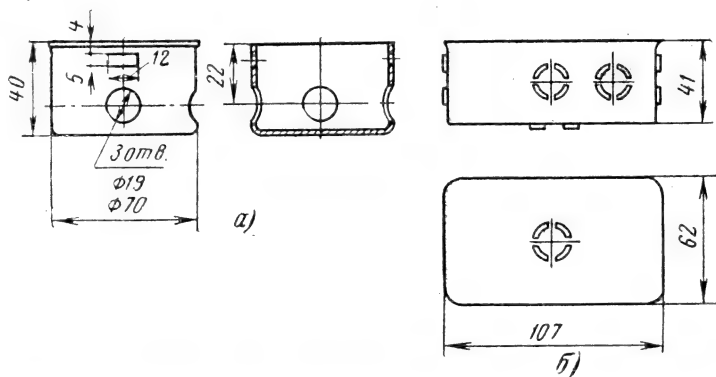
Коробки для установки выключателей и штепсельных розеток.
